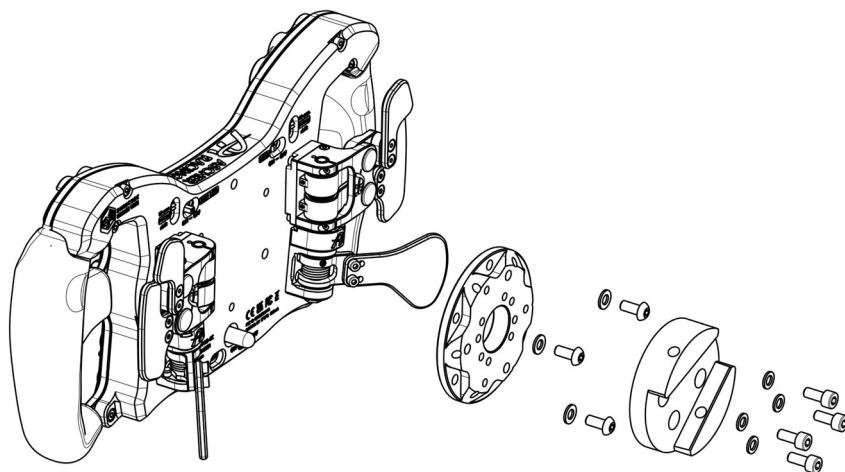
Montage des SC2 SQR WHEEL SIDE – Ascher Racing SQR Adapter
